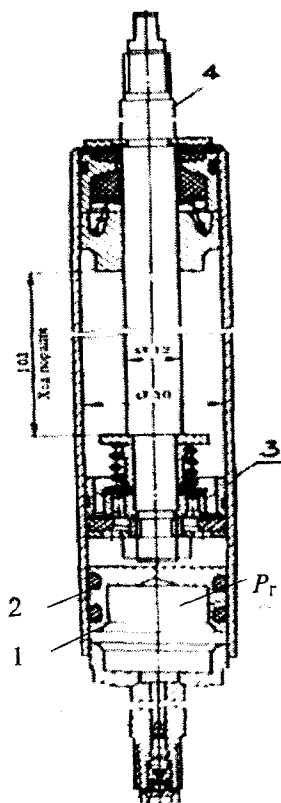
Однотрубный амортизатор грузового автомобиля КамАЗ:
